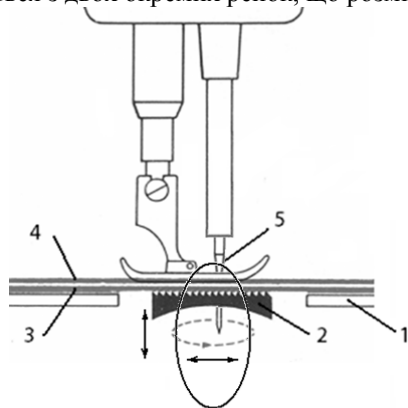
Безпосадочний механізм: 1 – голкова пластина; 2 – зубчатий пересувач; 3 – нижній шар тканини; 4 – верхній шар тканини; 5 – голка
